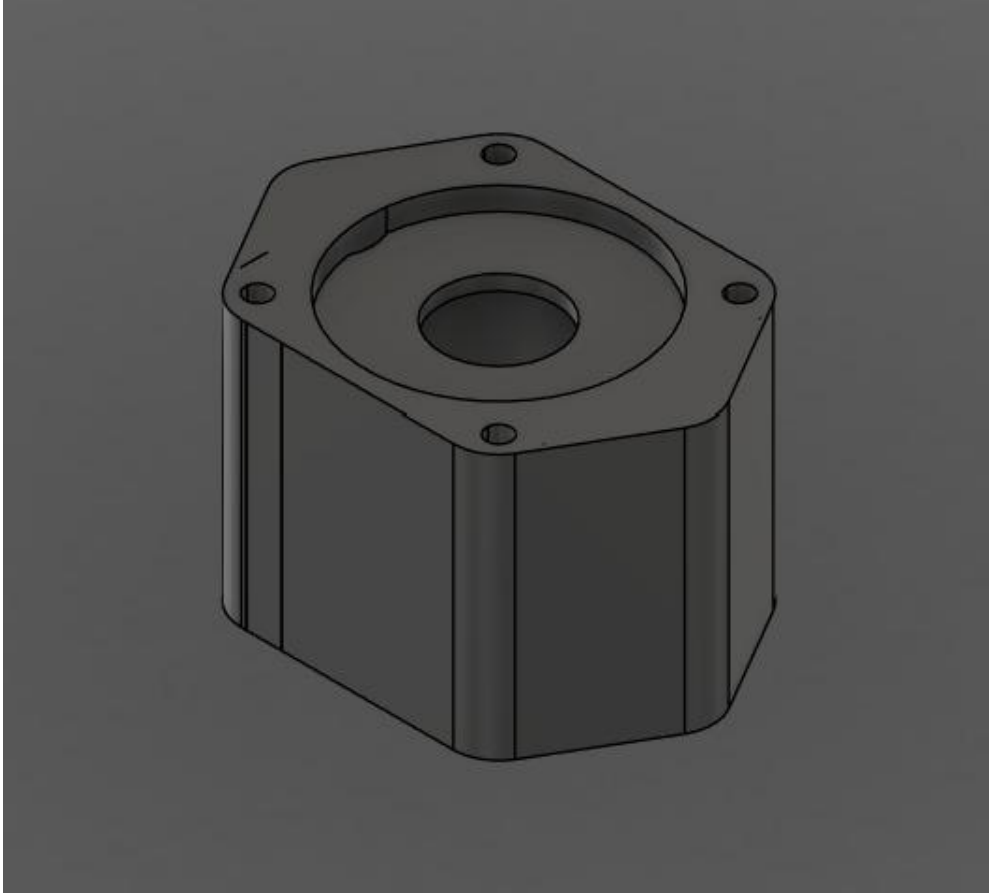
’de Mil-Servo motor ara bağlantı parçasının servo motora montelenmesi gösterilmektedir.
